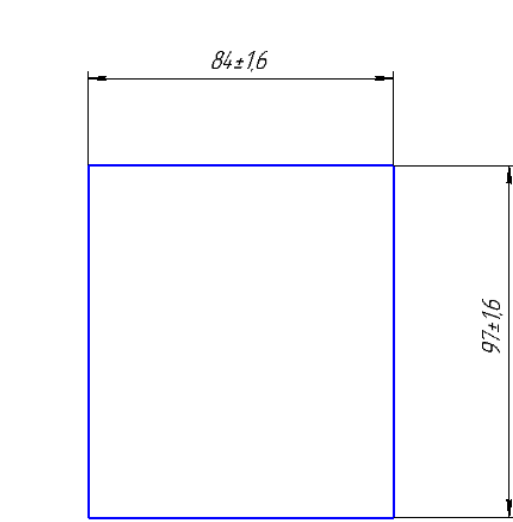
Схема заготовки для детали «Фланец».
